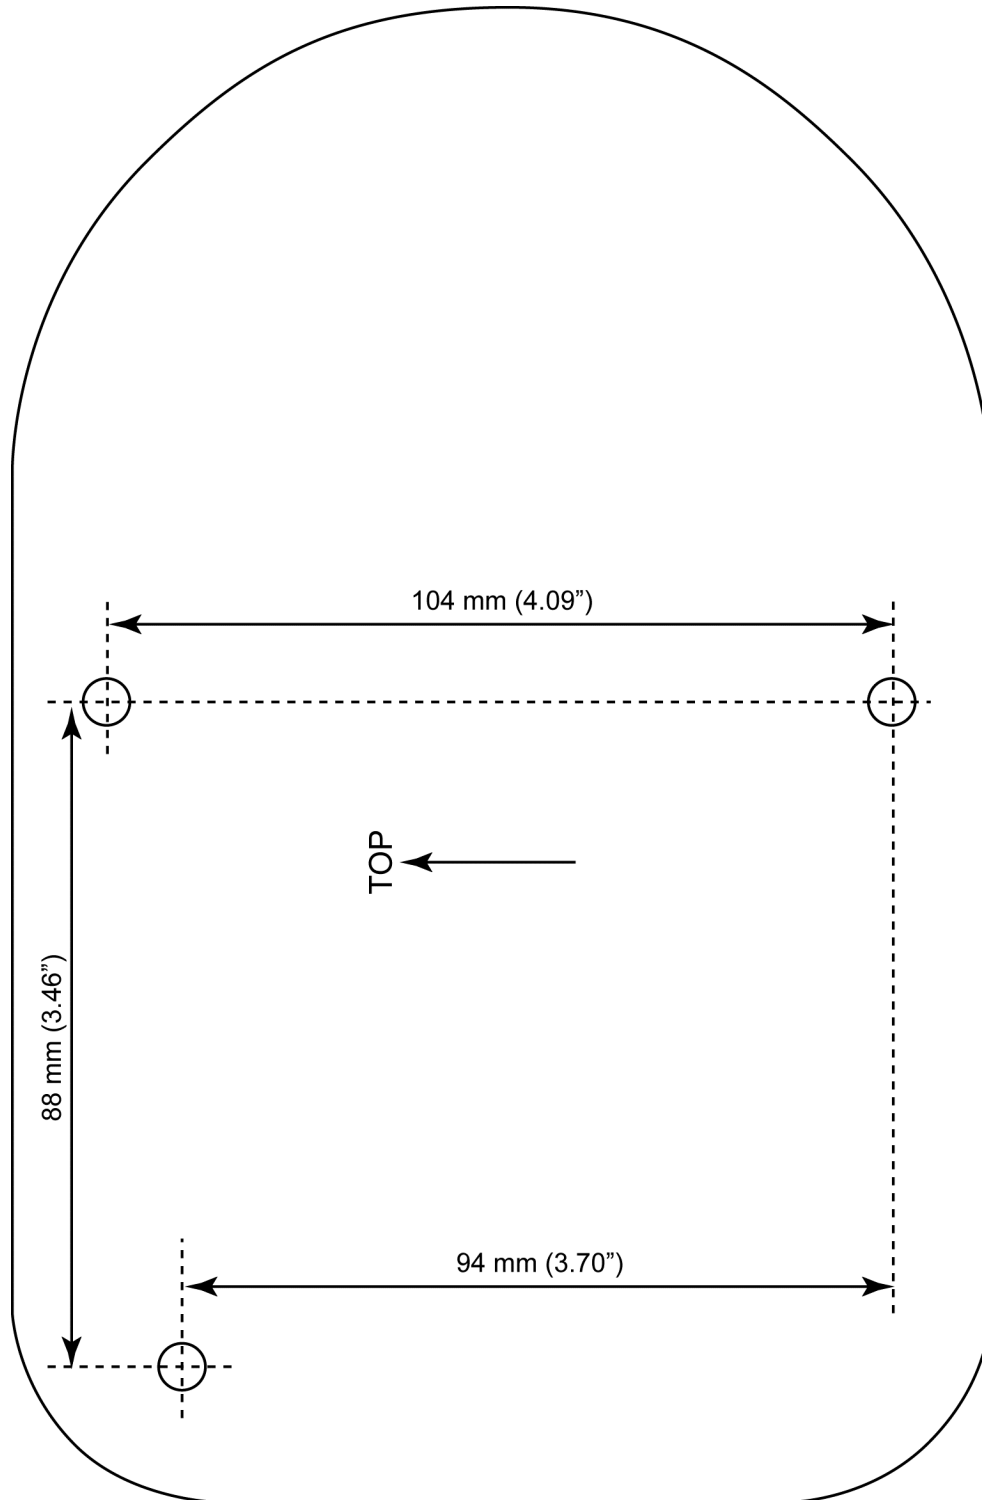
Bohrlochschablone der Bildsensor-Rückseite
